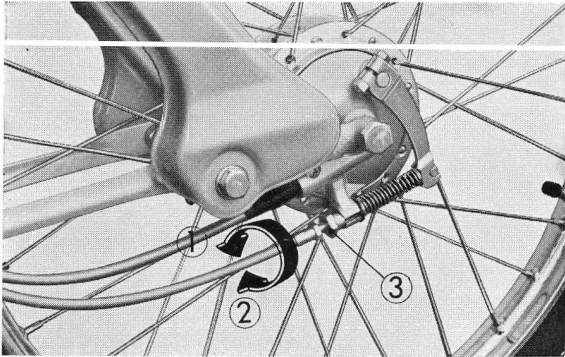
① pour augmenter la garde ② pour diminuer la garde ③ écrou de réglage
